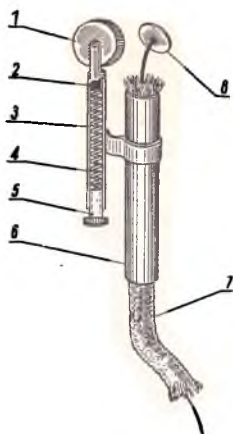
Искровая карманная зажигалка: 1 — огниво; 2 — кремнь из пиритового сплава; 3 — трубка искрового механизма; 4 — пружина; 5 — винт; 6 — фитильная обойма (гильза); 7 — фитиль; 8 — заглушка
